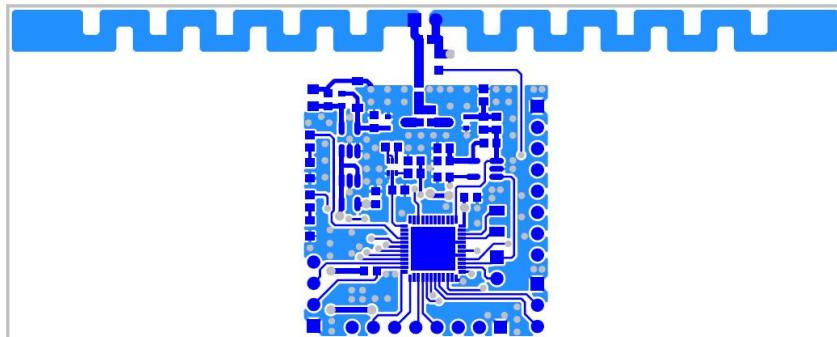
지능형 RFID 센서의 PCB 태그제품 아트웍
